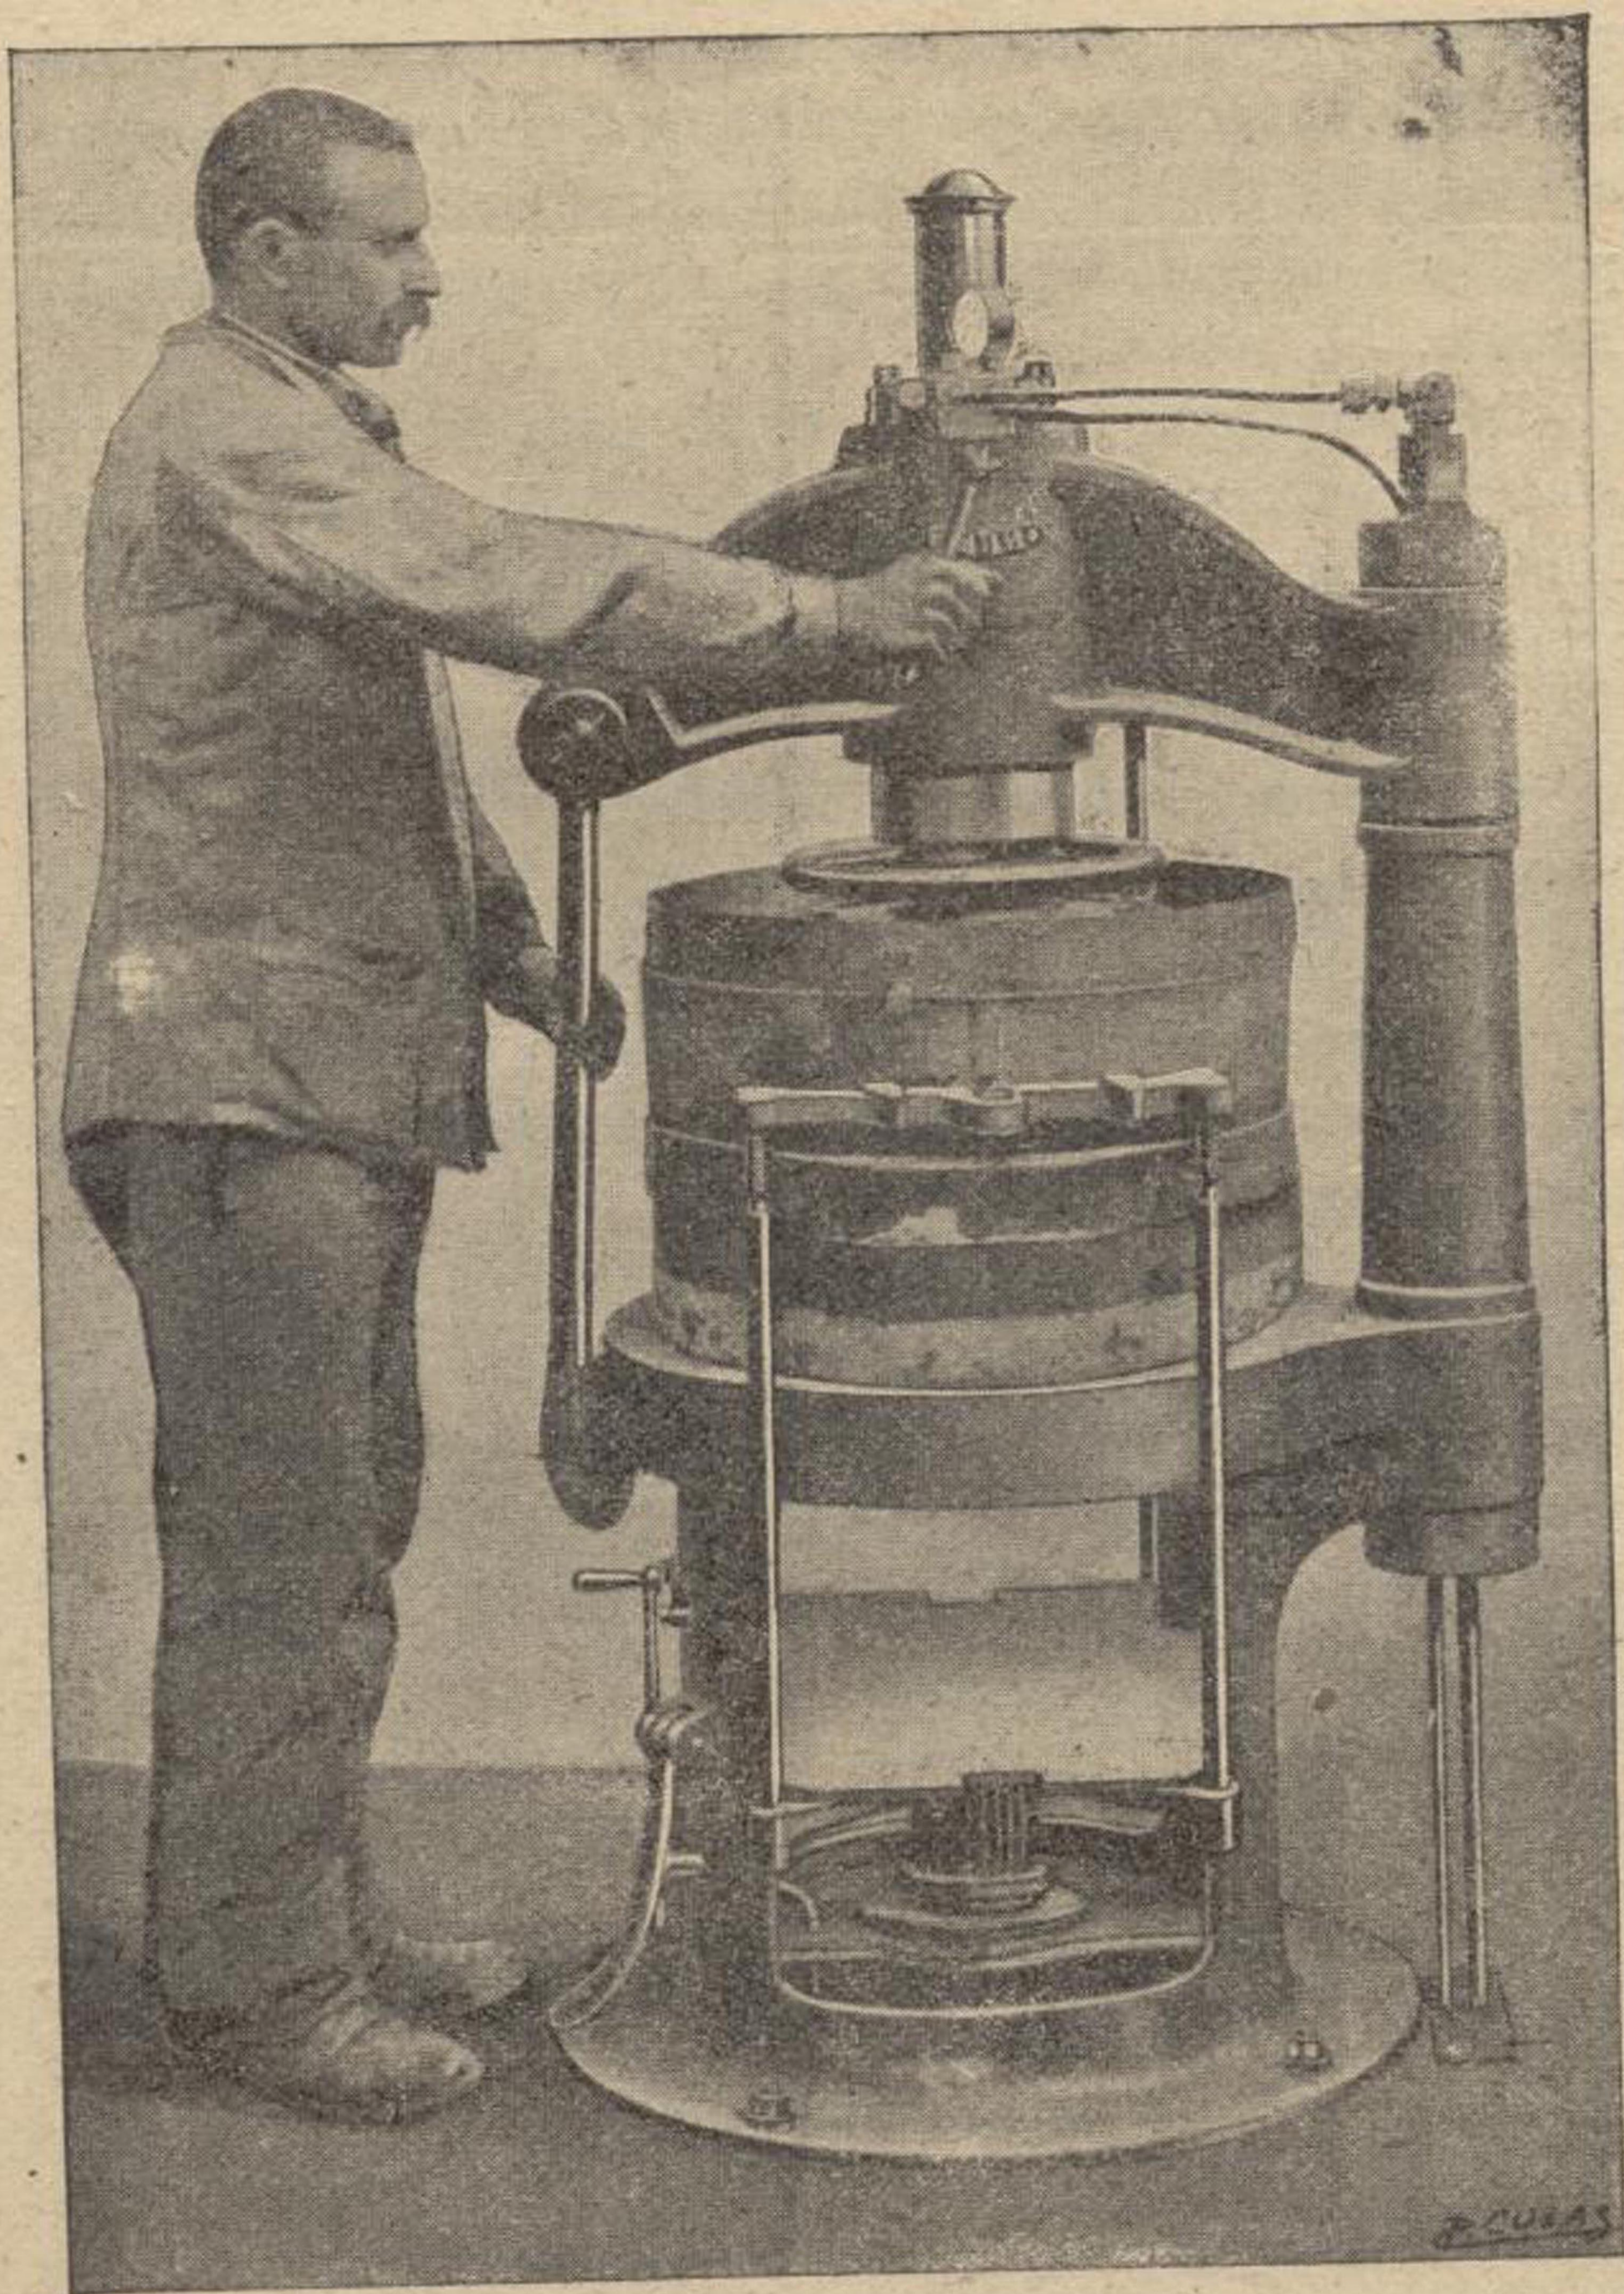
^a—Máquina de moldear hidráulica, tipo corriente
